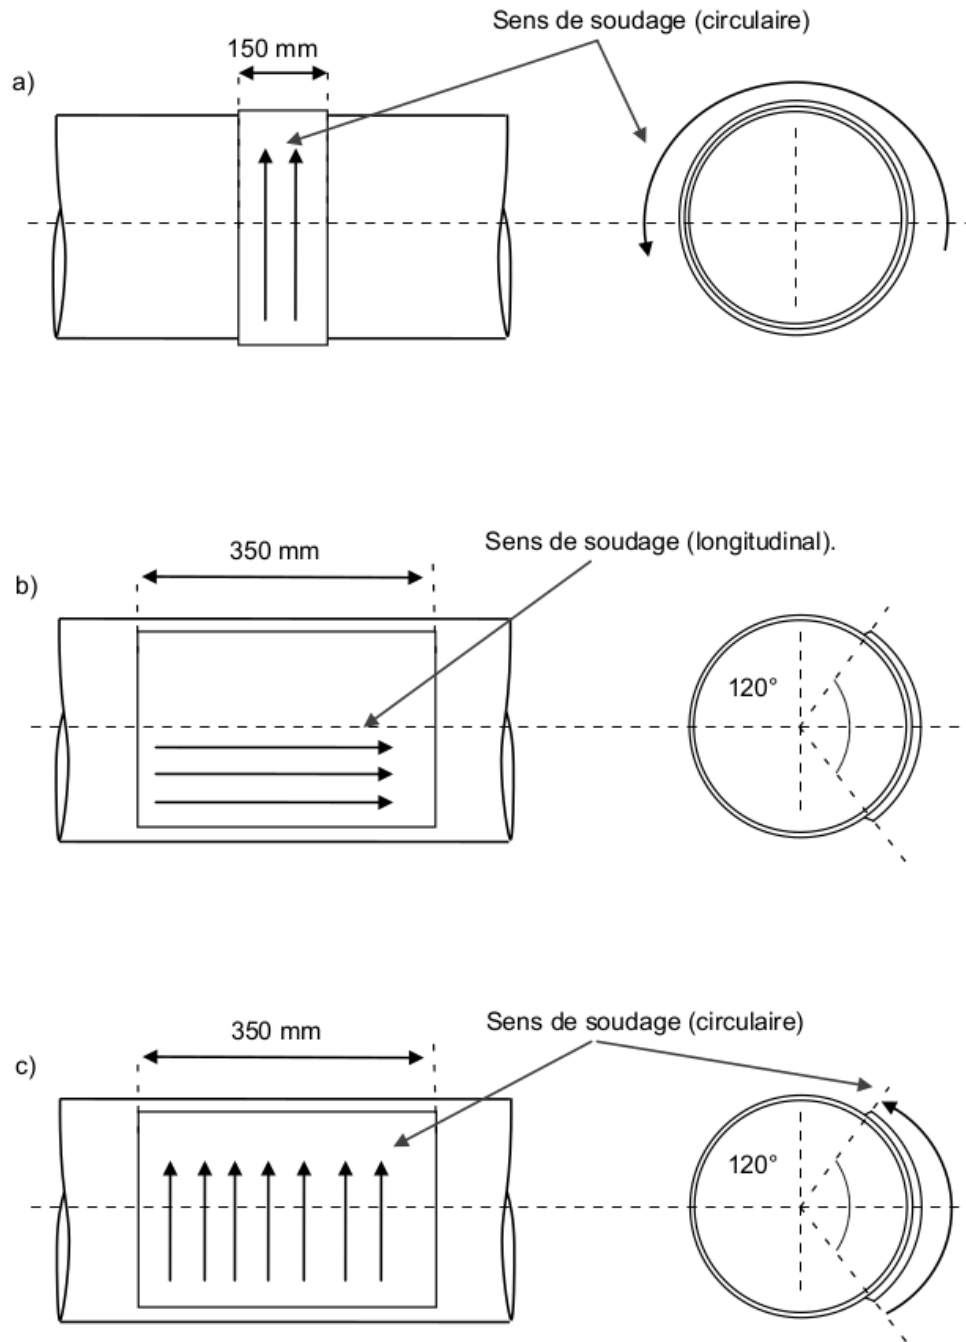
Schémas des rechargements sur tubes de 1900 mm, sans soudure DN300, d'épaisseur 12.8 mm et de matériau P265GH. a) Rechargement de type Overlay complet. b) Rechargement extérieur type Overlay partiel soudé à faible énergie. c) Rechargement extérieur type Overlay partiel soudé à haute énergie.[4].
